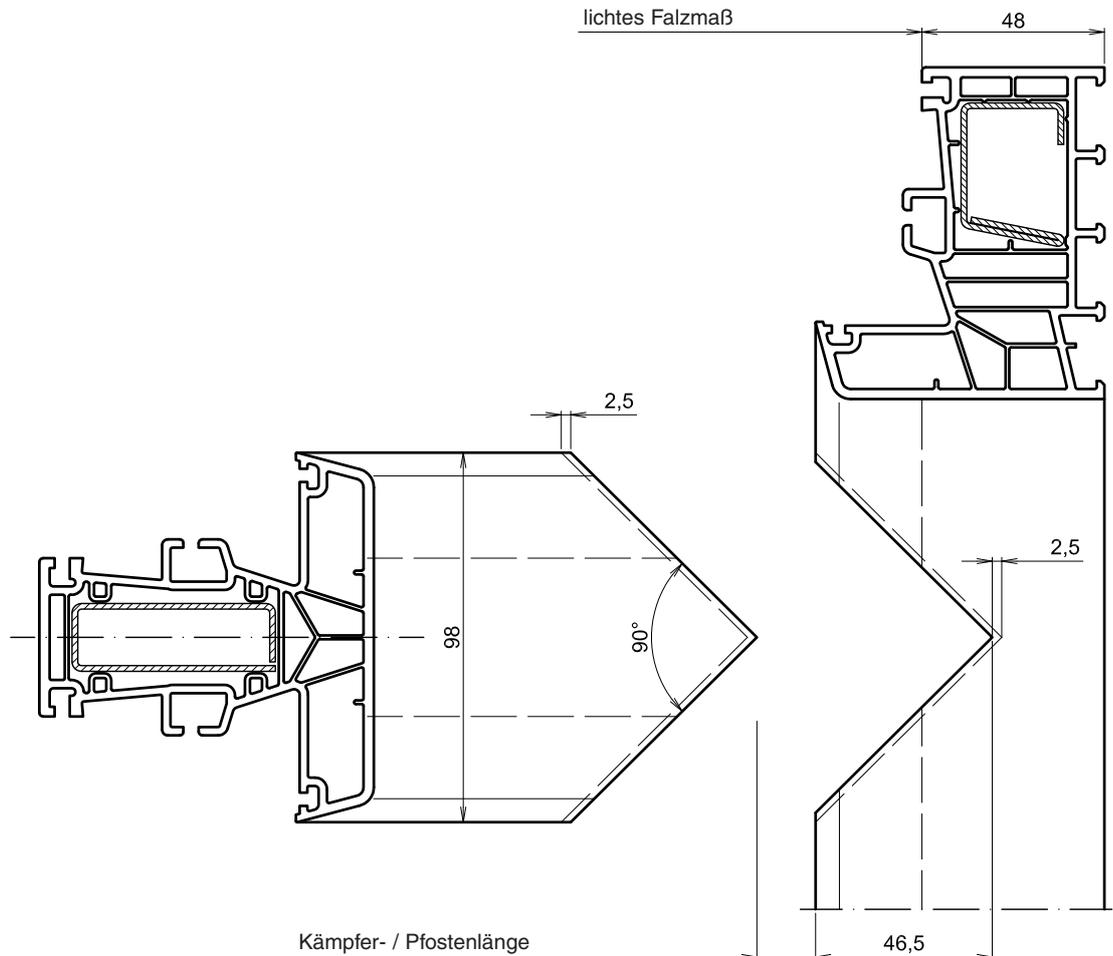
Einschweißmaße am Beispiel 6221.1
